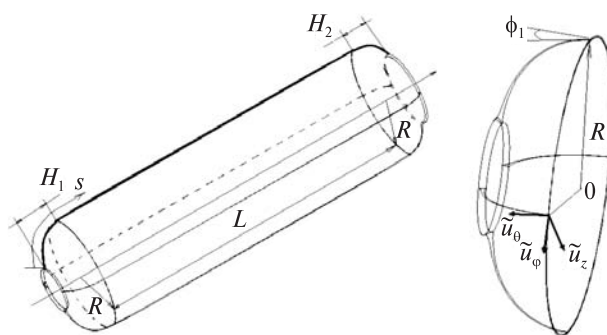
Эскиз корпуса твердотопливного двигателя и срединная поверхность левого днища
